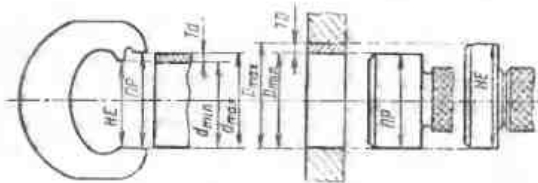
Схема, показывающая принцип проверки допусков деталей предельными калибрами.
